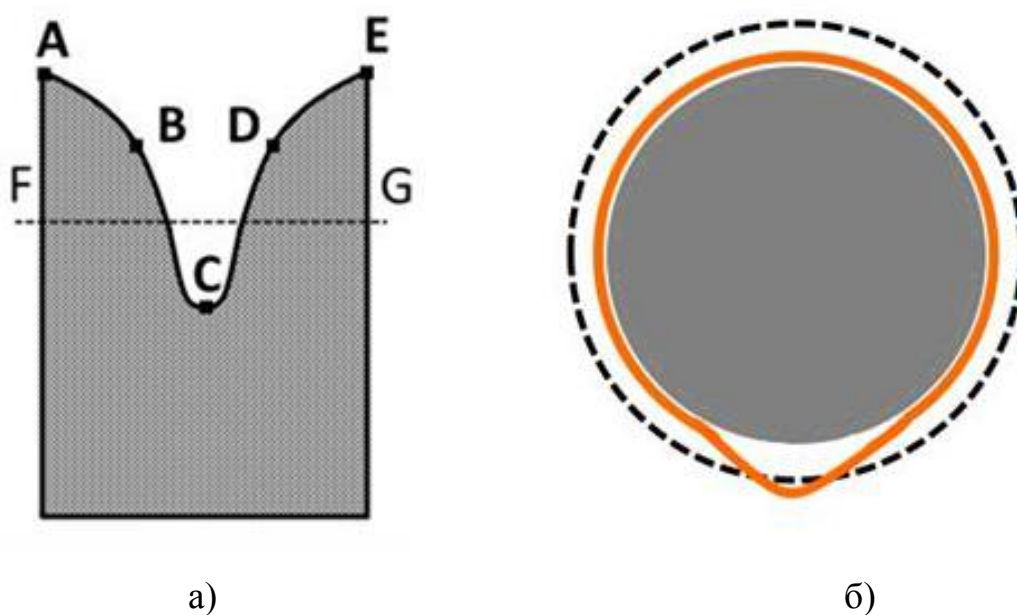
Схема утворення дефектів: (а) – розгортка фронту детонації ВР, розташованої на циліндричній поверхні; (б) – схема деформування мідної плакувальної труби в її поперековому перерізі, де штрихова лінія – первісна (до зварювання) форма перерізу труби, помаранчева лінія – форма перерізу труби на лінії FG (а), сіре коло – алюмінієвий стрижень
